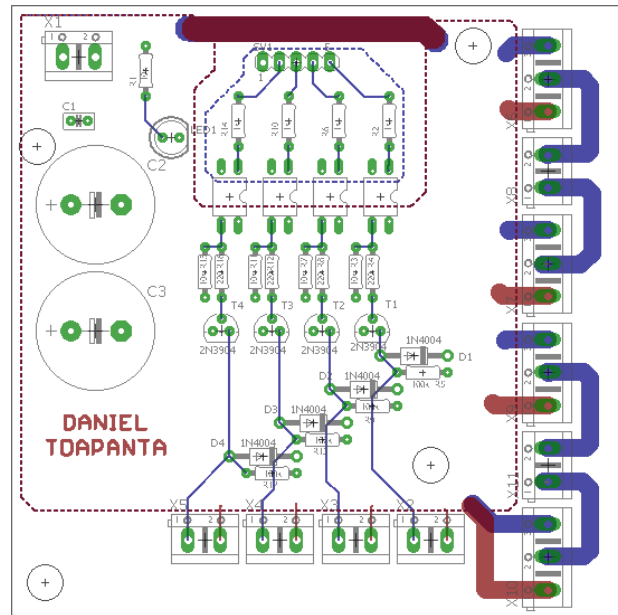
Diseño de placa de circuito de control de motores. [Autor]
